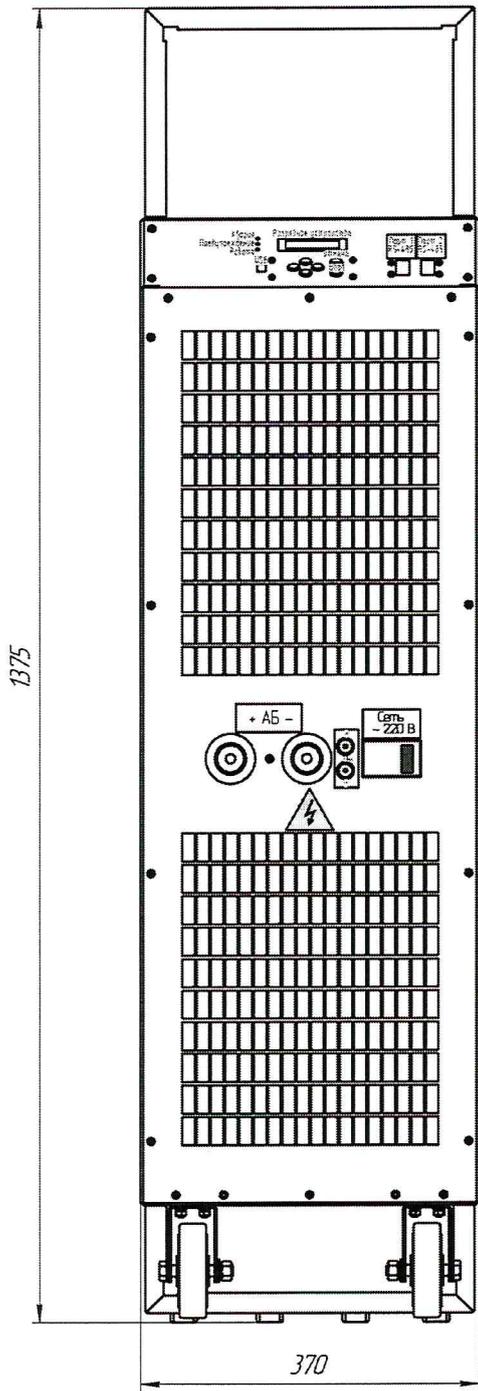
Общий вид и габаритные размеры СКР-200
